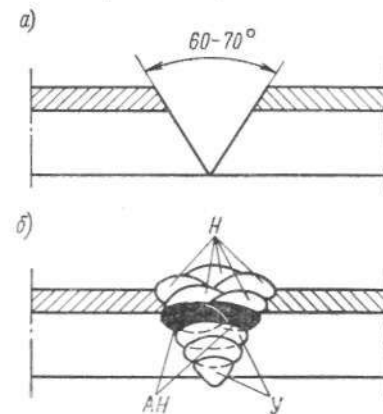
Стыковые соединения двухслойных сталей больших толщин с разделкой кромок со стороны нержавеющей стали: а — вид разделки кромок; б — выполненное соединение.
